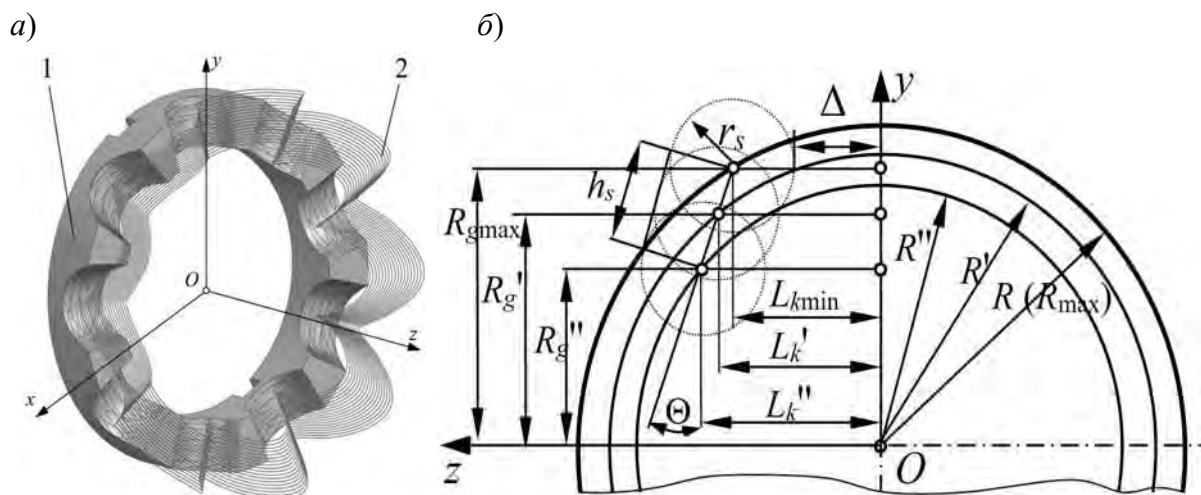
К пояснению способа изготовления зубьев сферической фрезой: а – общая схема обработки; б – геометрические параметры траекторий; 1 – колесо; 2 – траектории движения центра масс сферической фрезы
